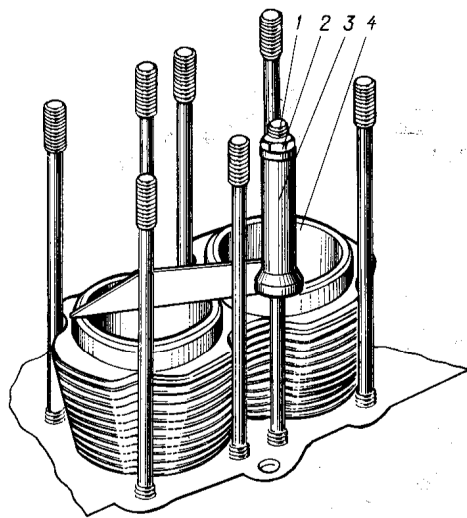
Приспособление для фиксации цилиндров на картере коленчатого вала:
